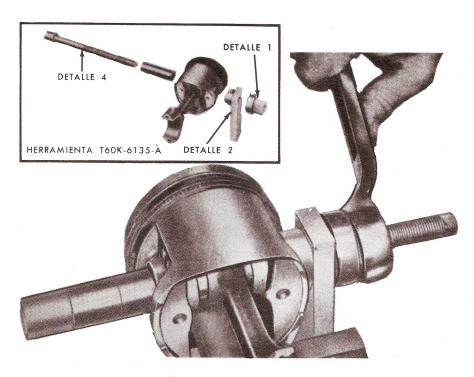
Desmontaje e Instalación de Pasadores de Pistón. Típico.
